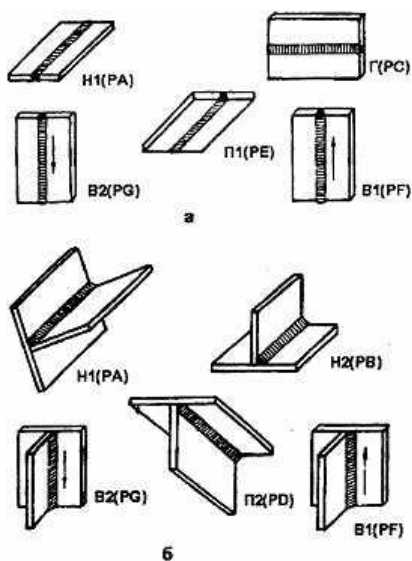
Положение шва при сварке стыковых (а) и тавровых (б) соединений листов:
